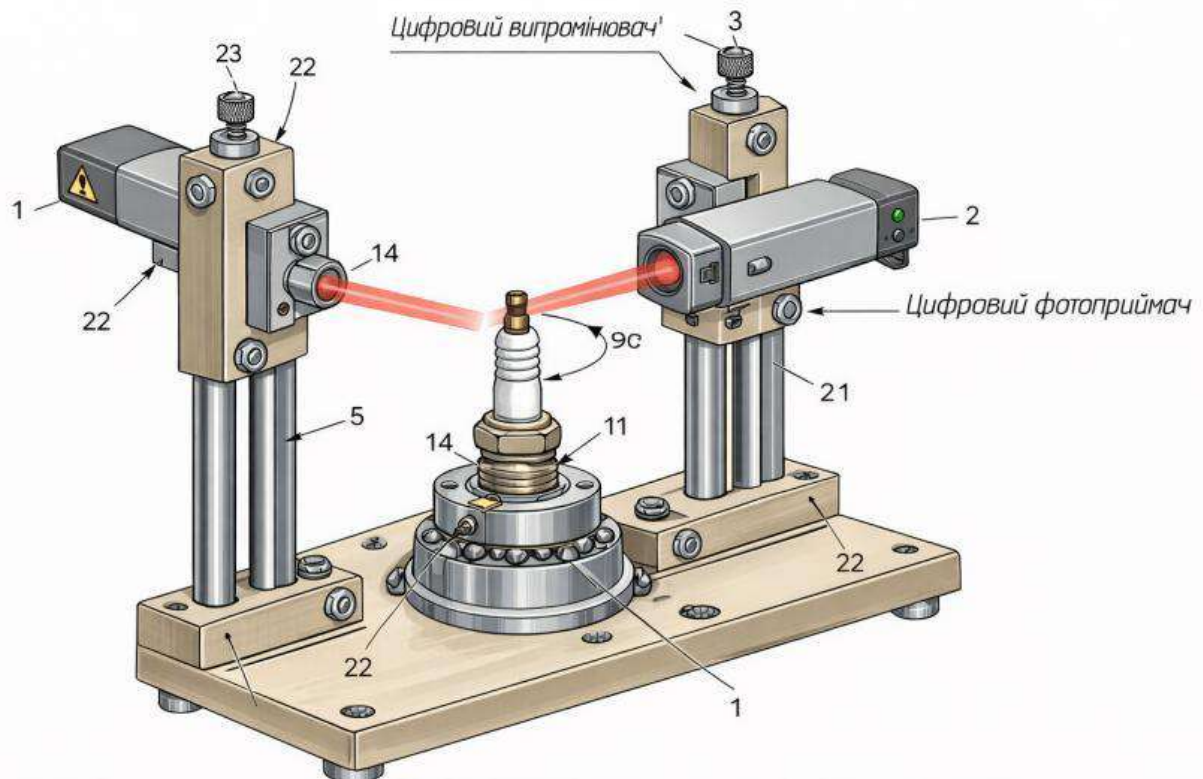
Пристрій автоматичного вимірювання зазору
